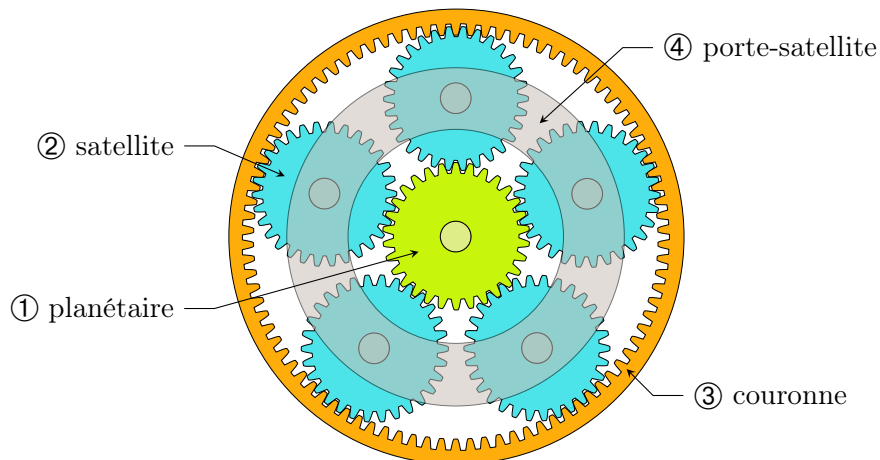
Schéma d’un réducteur à engrenages ou gearbox.
